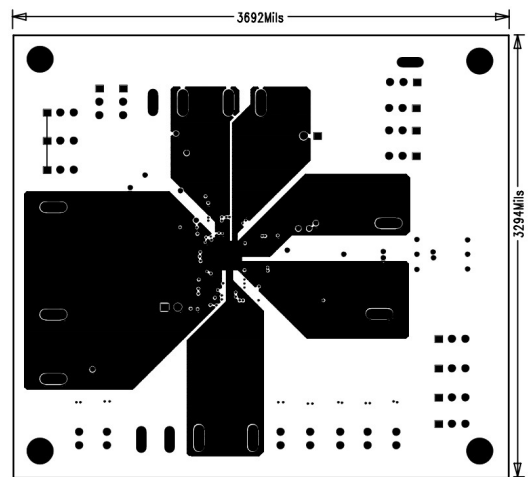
Max 8662 PCB LayOut - PGND Layer 2.
